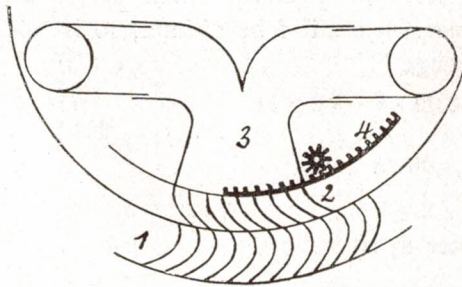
Regulierung der Girardturbine mit innerem Aufschlag.
